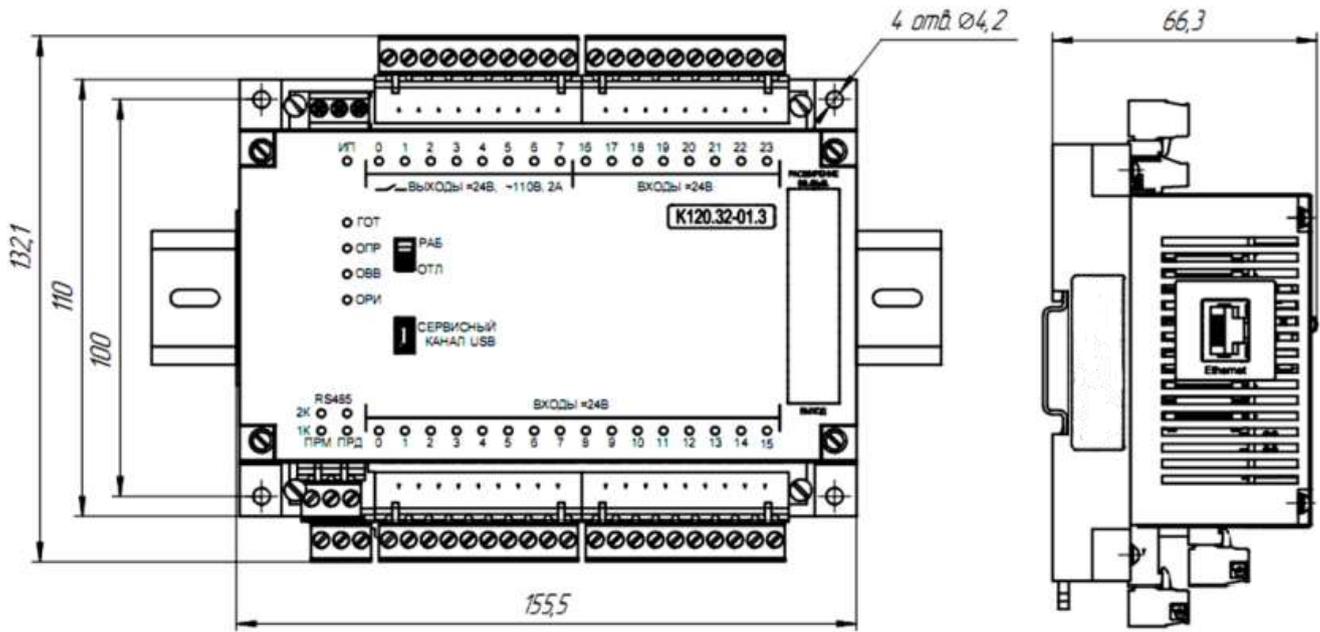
Габаритные и установочные размеры блока K120.32-01.3
